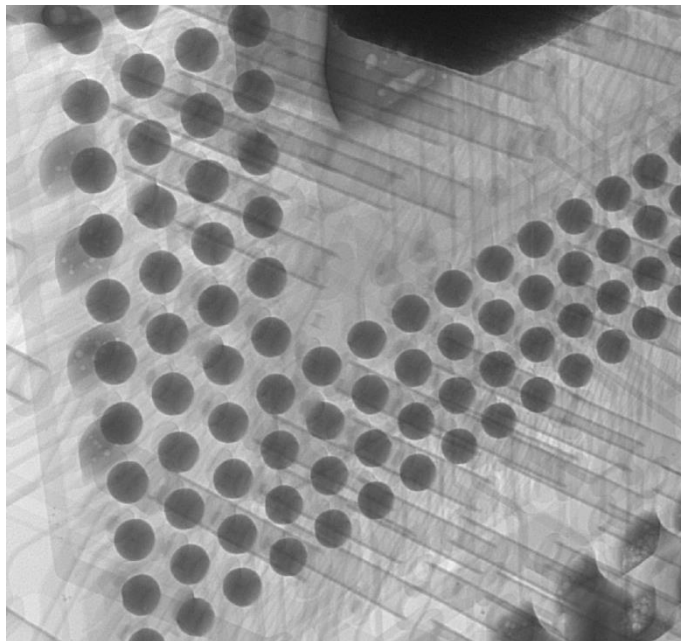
Vytvořený otisk v pájecí pastě od Fine Pitch BGA komponentu v aplikačním přípravku
